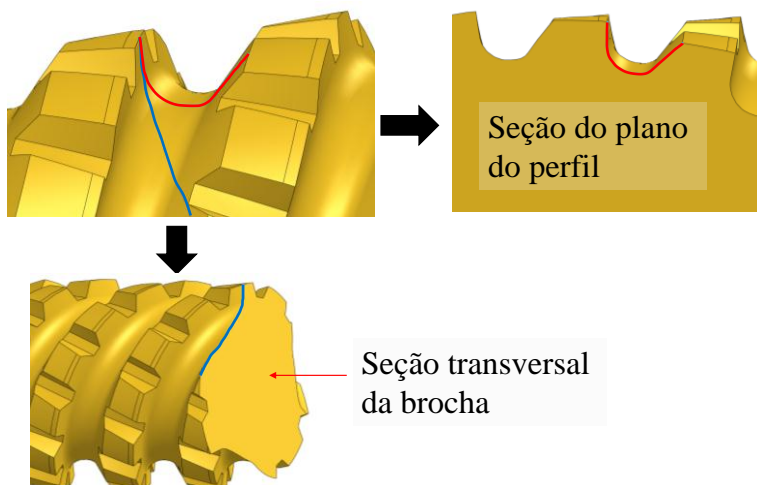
Projeção do perfil dos canais sobre o plano transversal.
